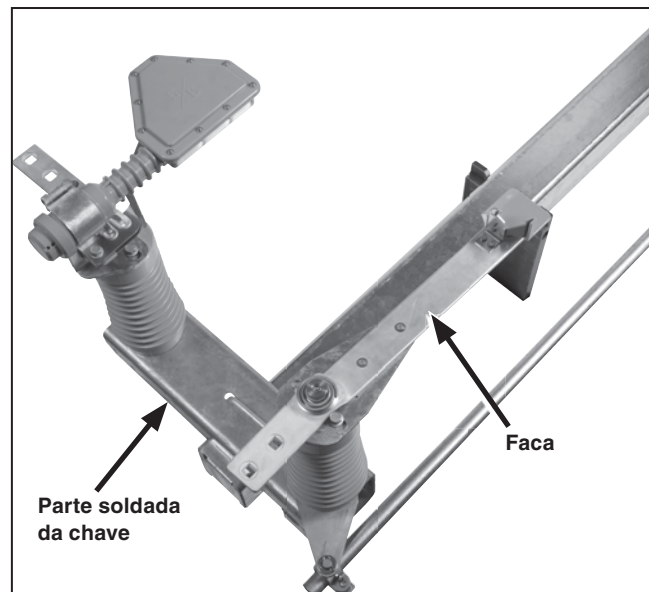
Faca a 90 graus da posição soldada da chave.
